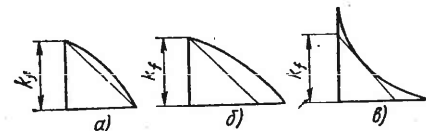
Схемы сечений сварных угловых швов:
